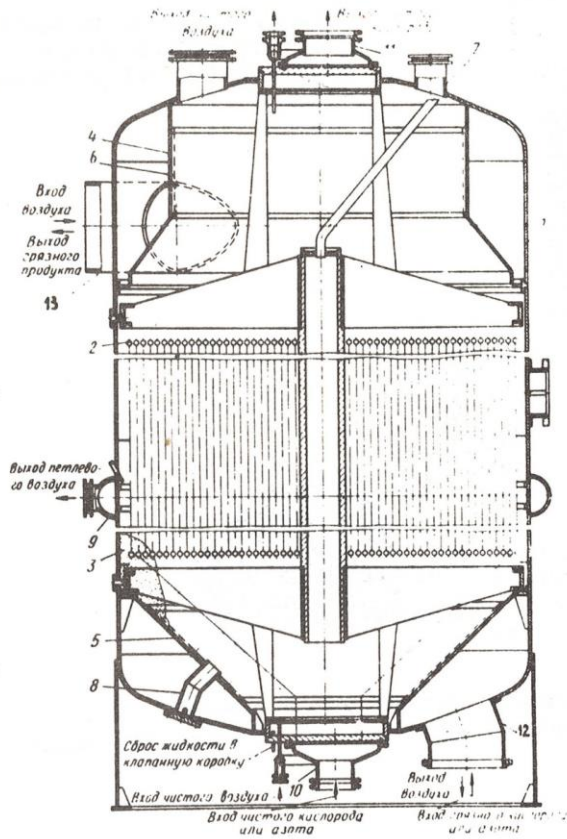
Регенератор с засыпной насадкой и встроенным змеевиком. 1-корпус, 2-змеевик; 3-насадка; 4-обечайка; 5-конус; 6-сетка; 7, 8, 9, 10, 11, 12, 13 - патрубки.
